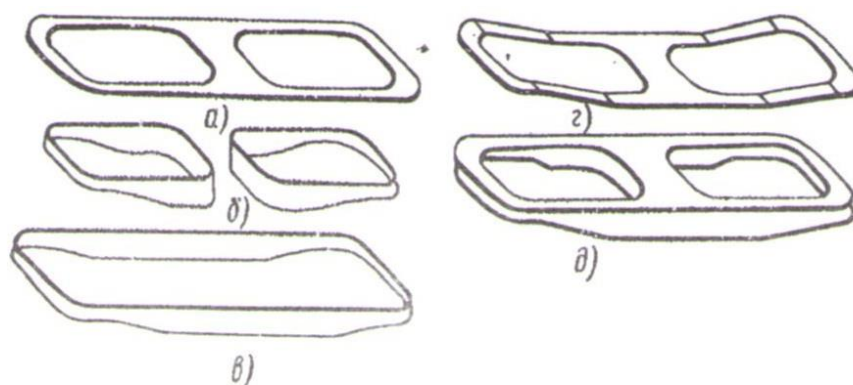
Последовательность сборочно-сварочных операций при изготовлении рамы
